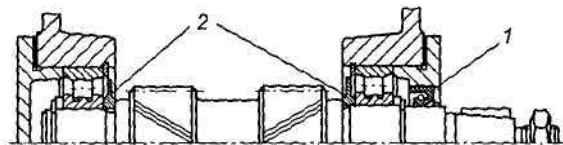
Схема установки вала, когда осевая нагрузка на вал не передается:
